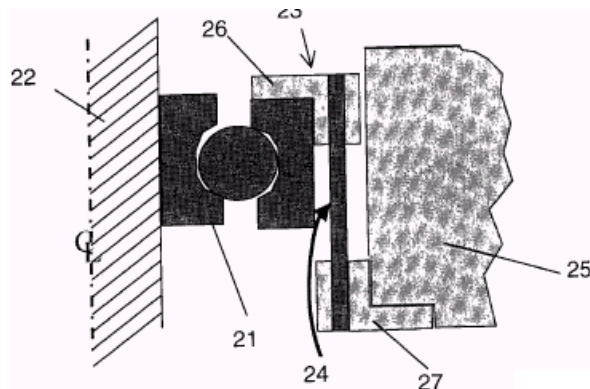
Конструкция подшипникового узла по патенту № GB2415019:
